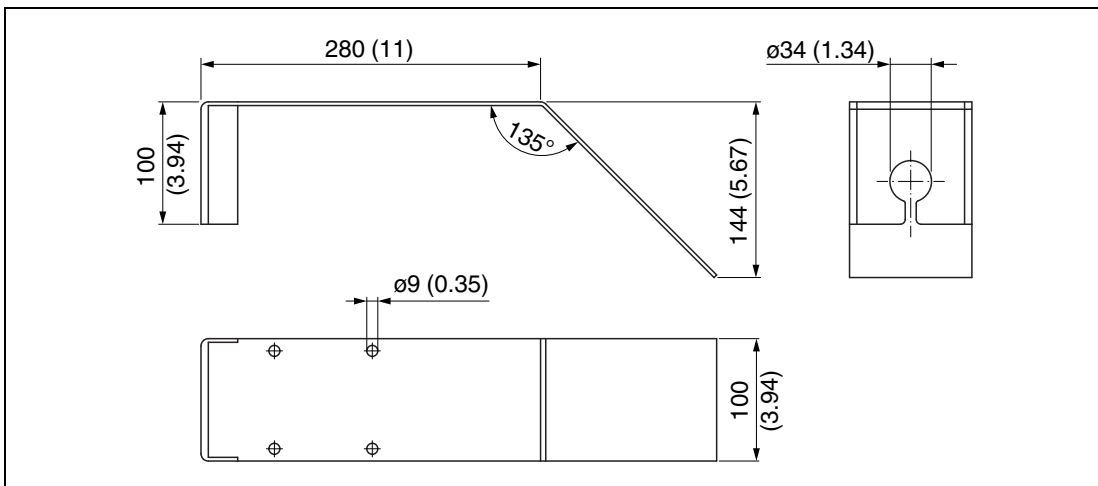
Abmessungen Horizontale Montagehalterung Abwasserschacht, Maßeinheit: mm (Zoll)
